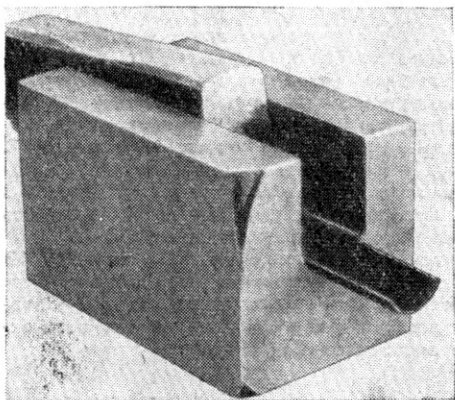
Штампы для изготовления лопаток вентиляторного колеса (слева)
